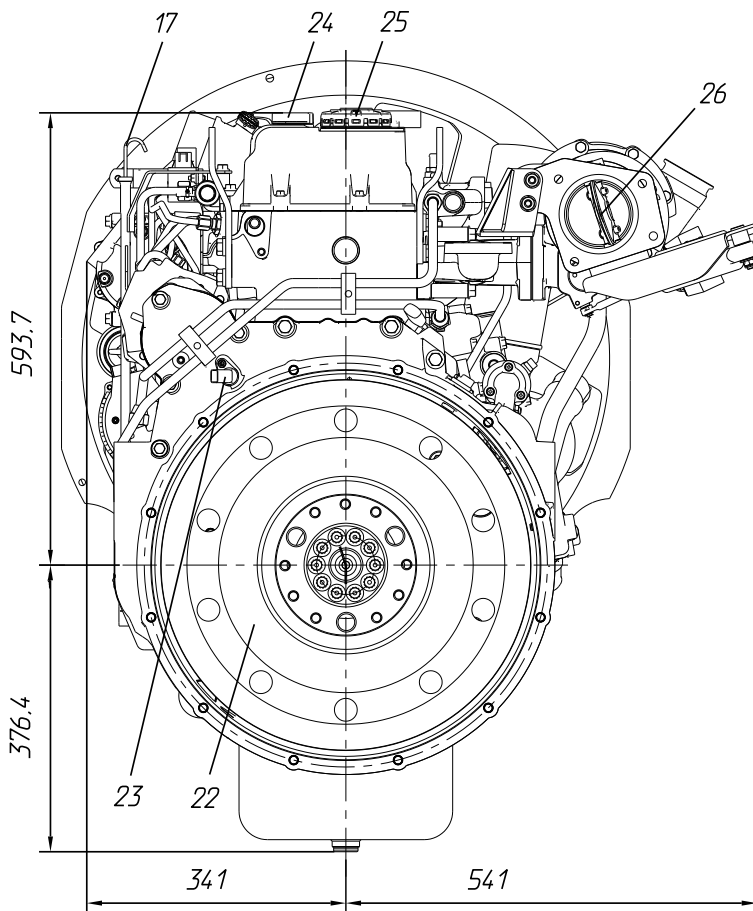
Габаритные размеры, расположение агрегатов и узлов двигателя ЯМЗ-5367 (вид сзади):
